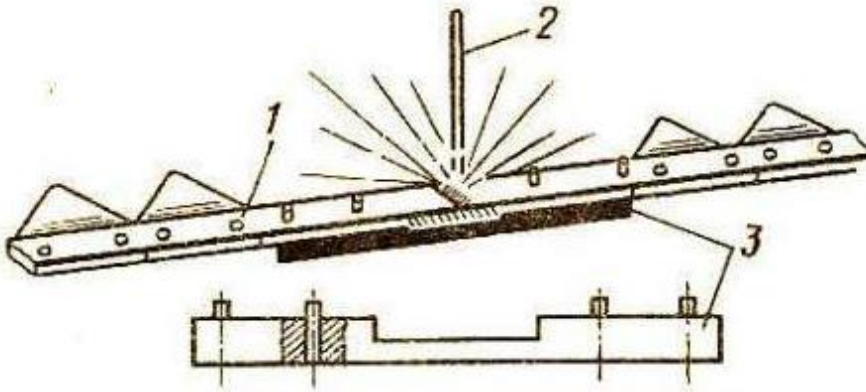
Схема зварювання спинки ножа в кондукторі:
